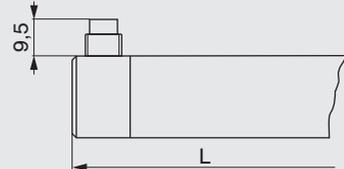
Wegsensor Typ - SR mit radialer Steckverbindung
